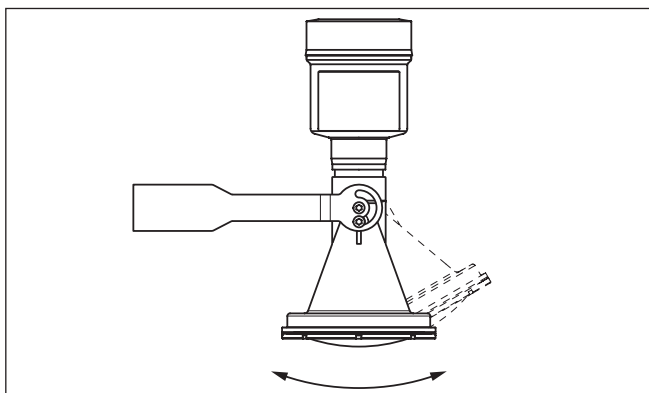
Ajuste de la inclinación durante el montaje horizontalmente en la pared
